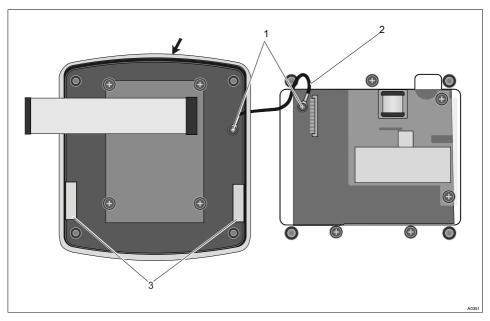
Установка профильного уплотнения на верхней части корпуса регулятора
